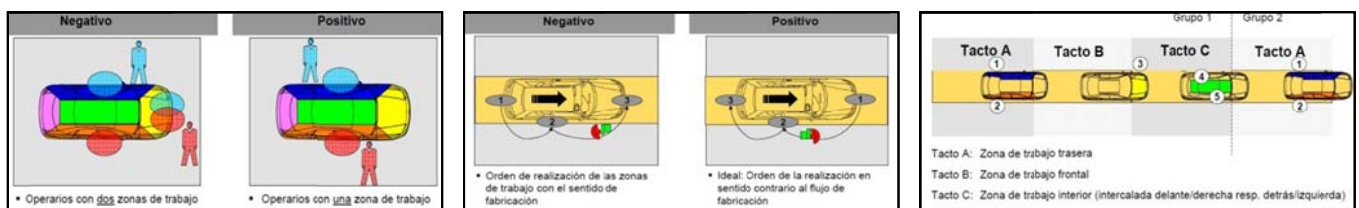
Zonas y secuencia de trabajo
